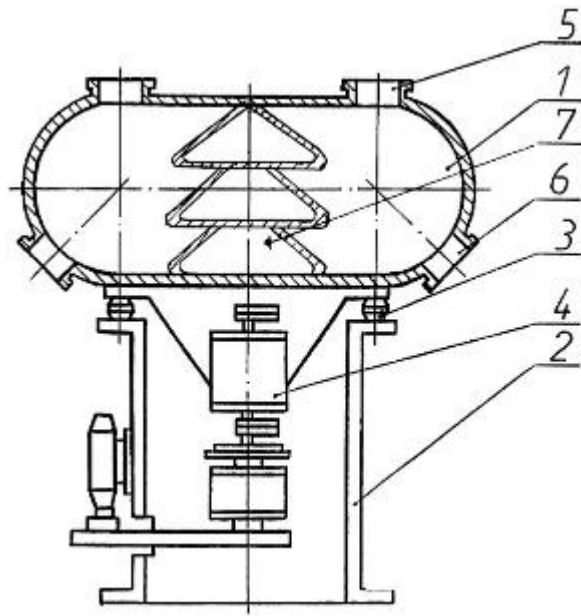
Вібраційний змішувач з торовидною камерою змішування
